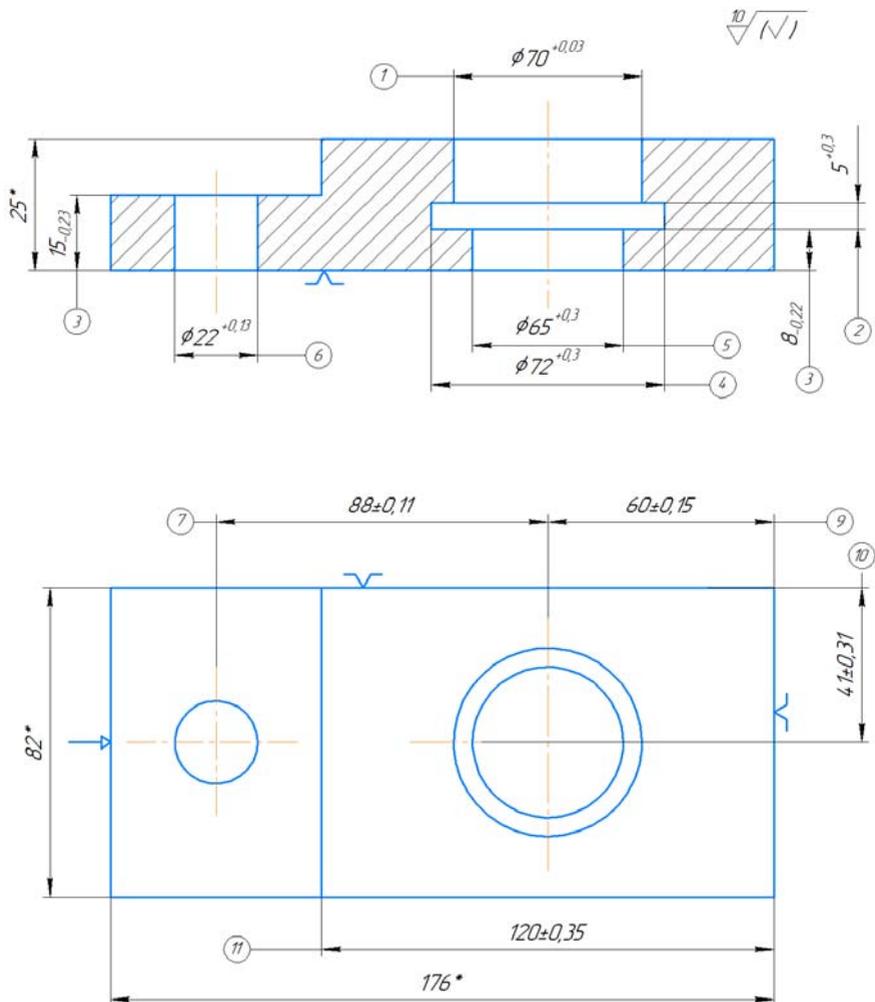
Эскизы заготовки из стали 20 и комплексной операции обработки детали «Плита» на станке модели 2254ВМФ4
